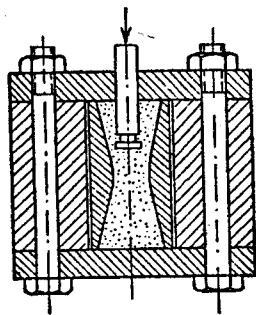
Приспособление для раздачи пальцев с конусным отверстием
